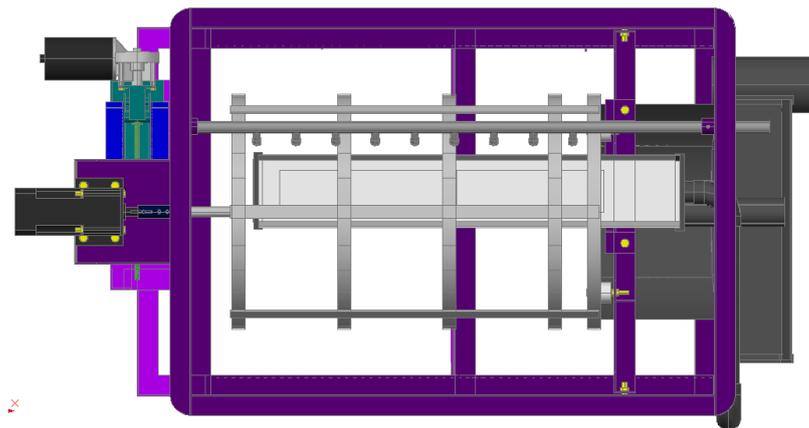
5 Komponen Mesin *Rotary Drum Filter* 3M (2)
